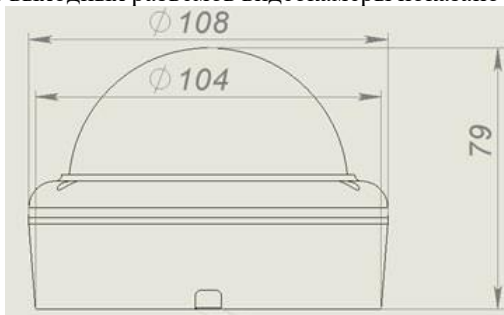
Внешний вид видеокамеры EVM2-IPx корпус KP24
